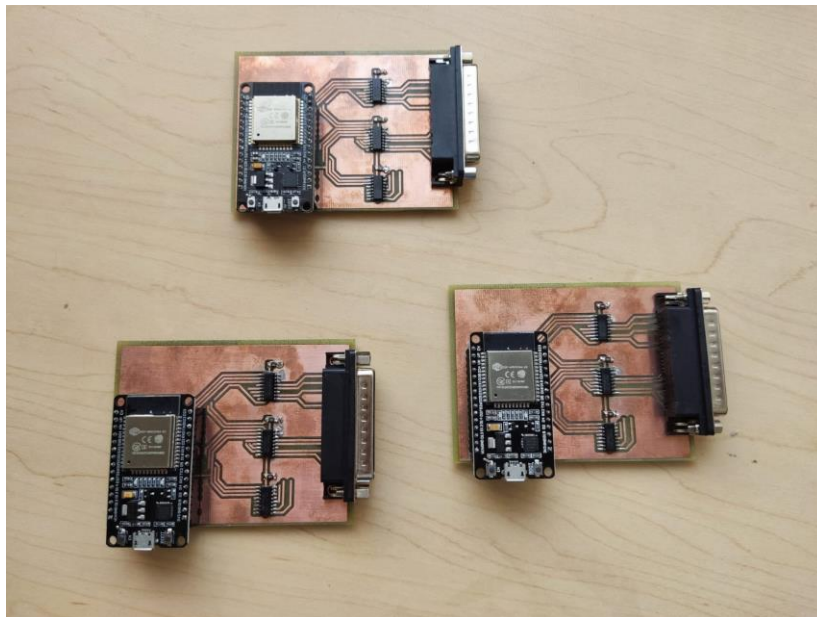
Nuevas placas soldadas junto a tarjeta ESP32.
